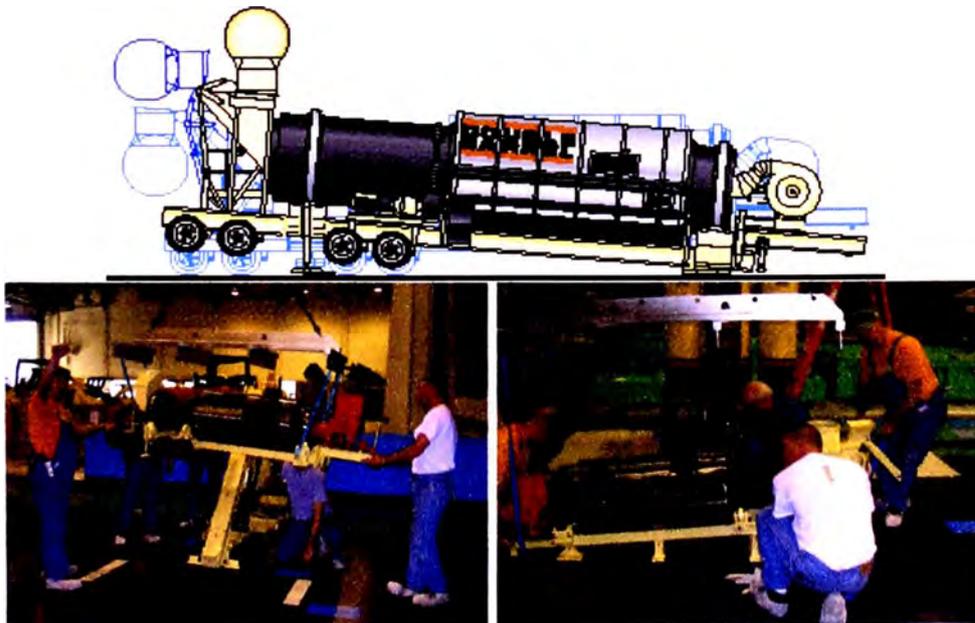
Réplica de la facilidad en el montaje del tambor mezclador Double Barrel de la planta de Asfalto ASTEC
